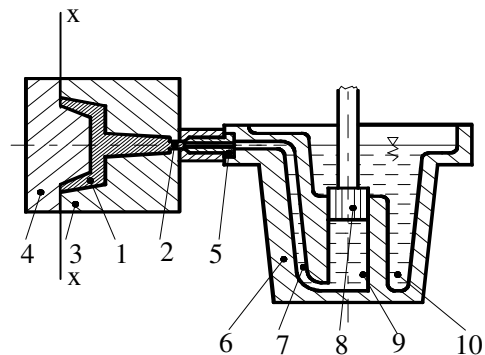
Mașina de turnat cu cameră caldă cu piston vertical:
